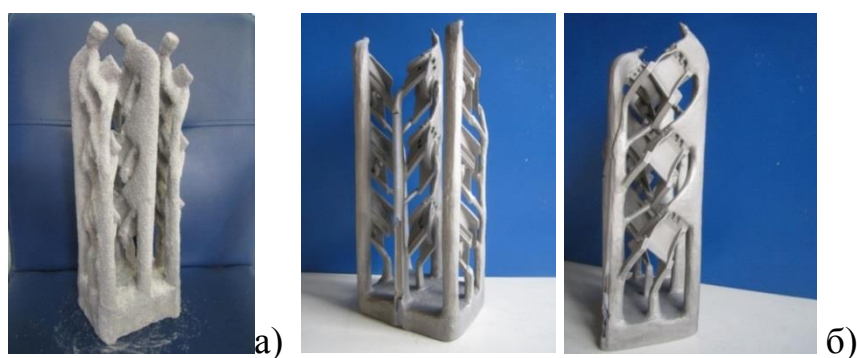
Литейный блок (а) и полученные отливки сопловых лопаток (б) из сплава ВИНЗ
